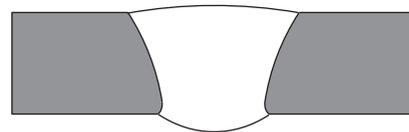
Exemple de soudure incorrecte n° 4
